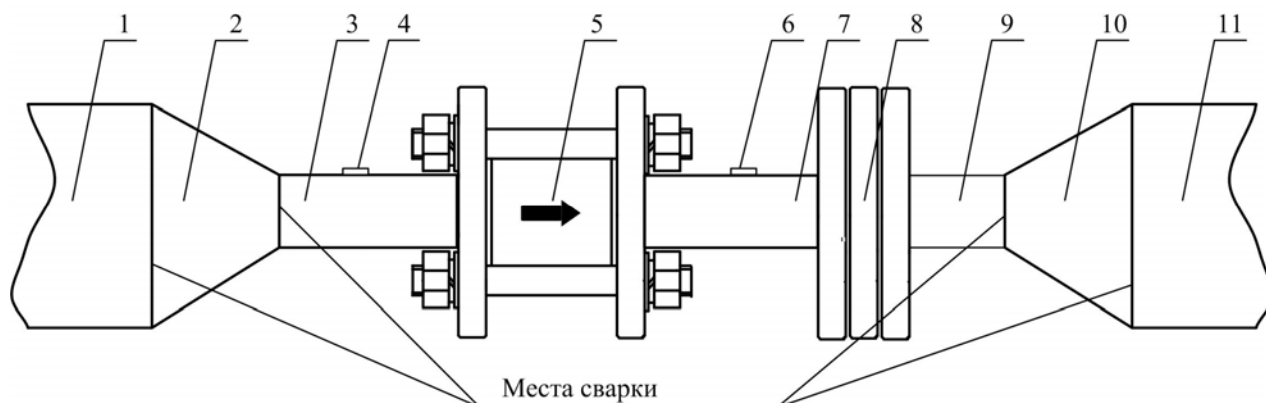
Вариант сборно-сварной конструкции с конфузуром и диффузором.
